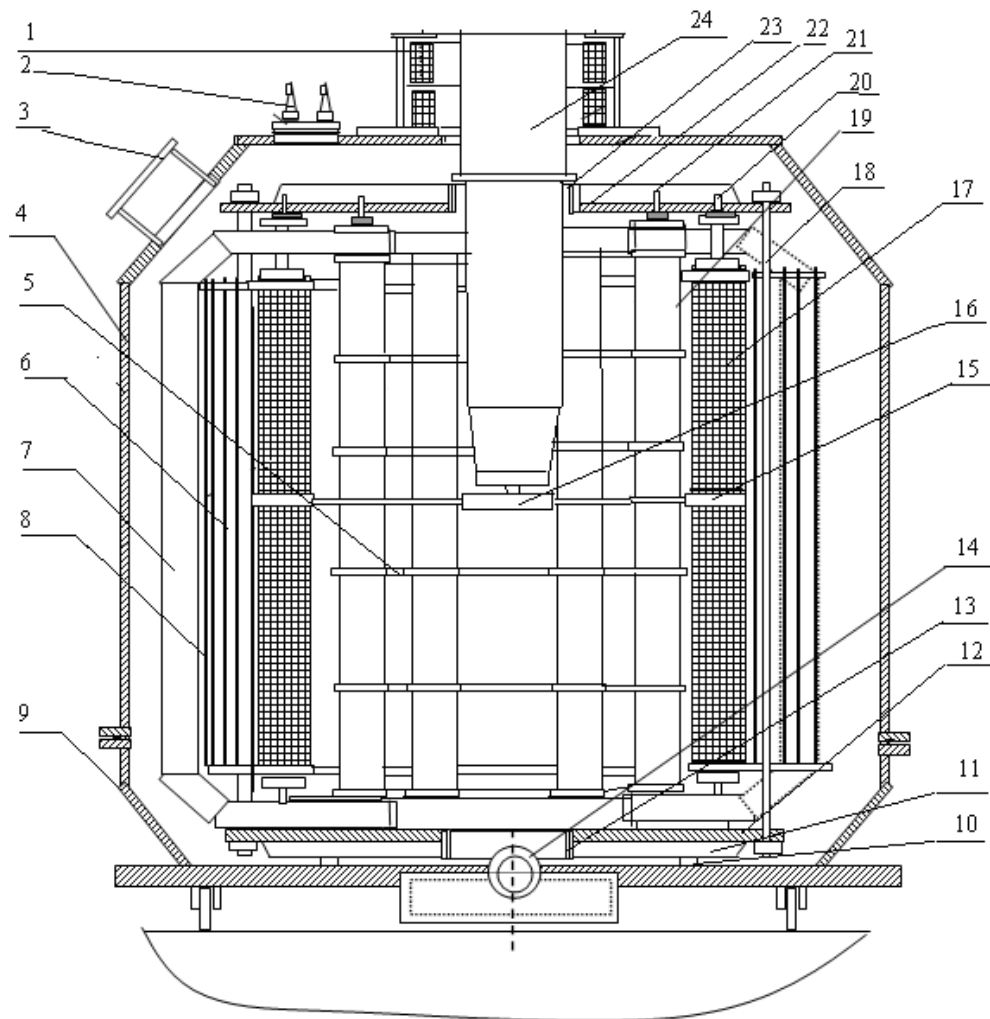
Принципова схема конструкції реактора РОДЦ 110 000 / 750
